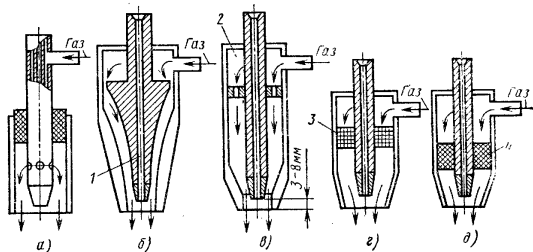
Схемы питания газом сварочных горелок:
